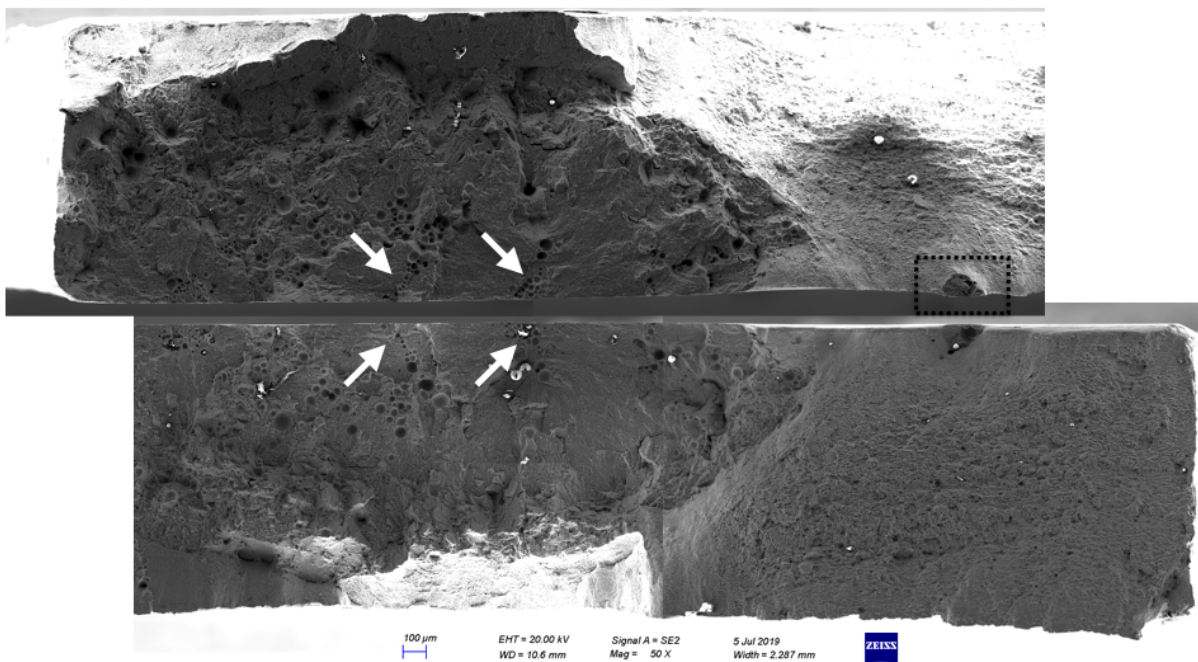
Fractographie de l'éprouvette 24A-4.
